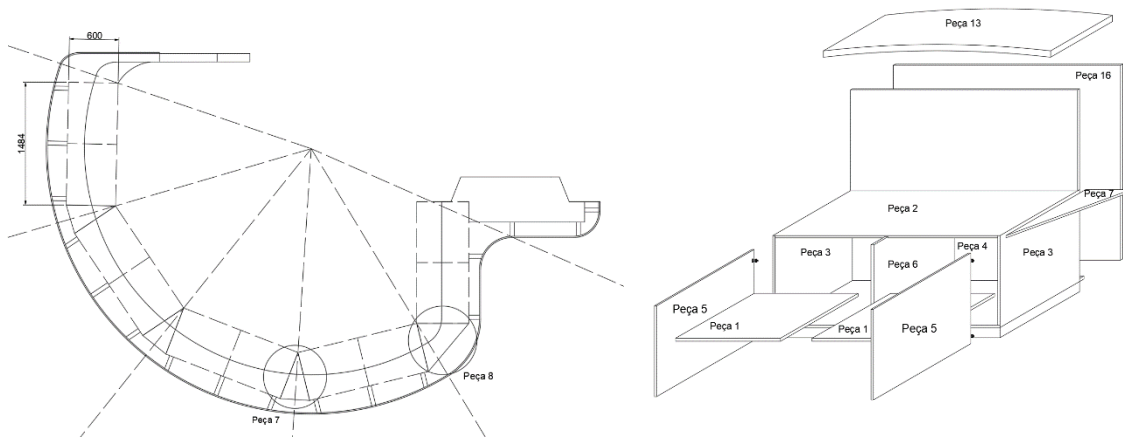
Desenho técnico de vista e axonometria explodida do bar. Fonte: Beatriz Guerreiro
